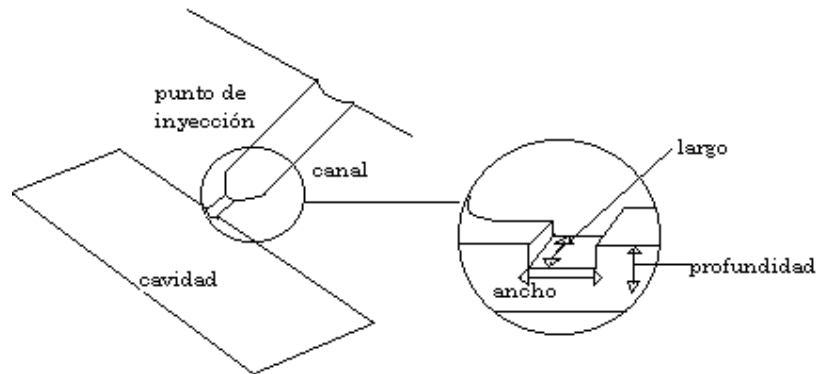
Dimensiones del punto de inyección⁽¹⁰⁾
